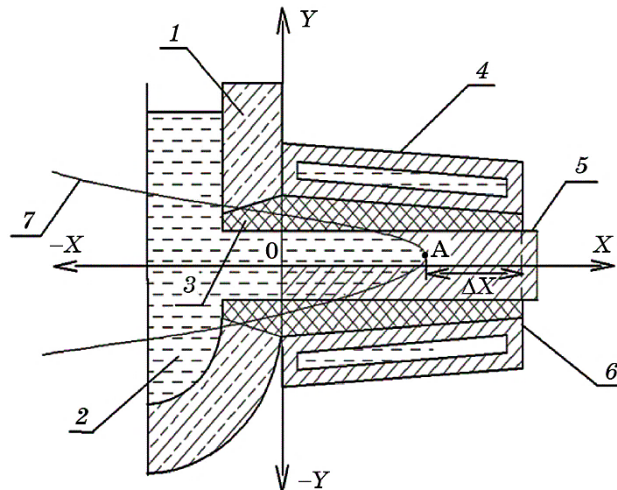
Вузол твердіння (кристалізації) ГМБЛЗ із мідних стопів [3]: 1 — корпус металоприймача, 2 — рідкий розтоп, 3 — графітова втулка кристалізатора, 4 — кожух з водяним охолодженням для примусового відбору тепла від заготовки, 5 — заготовка, що затверділа, 6 — вихідний торець кристалізатора, 7 — траєкторія твірних ліній.
